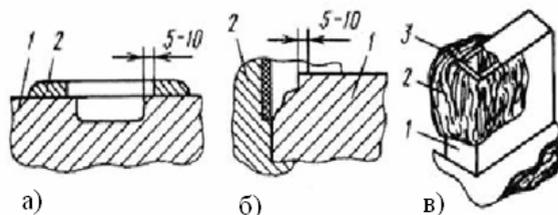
Формовка места сварки для горячей сварки чугуна:
